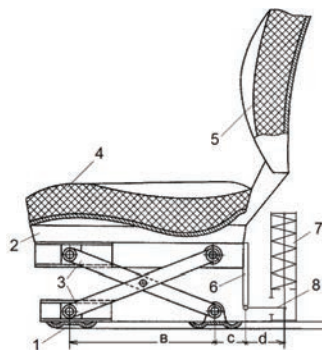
б. Общий вид подвески сиденья с направляющим механизмом типа «ножницы».
